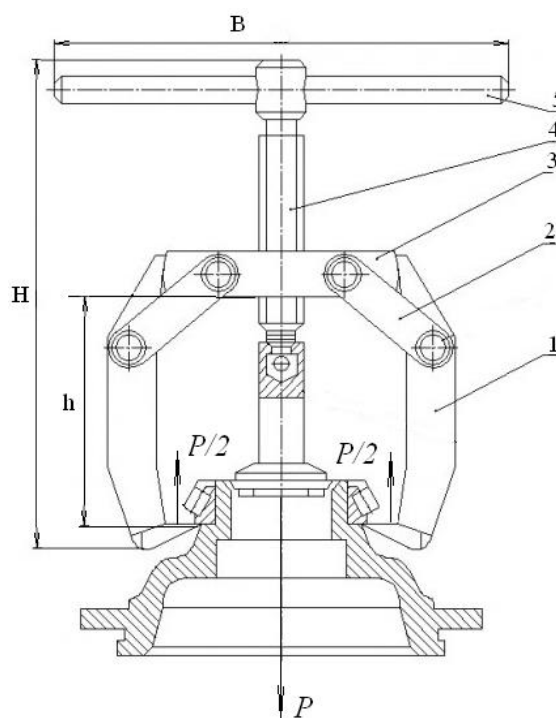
Винтовой съемник с лапчатыми захватами:
